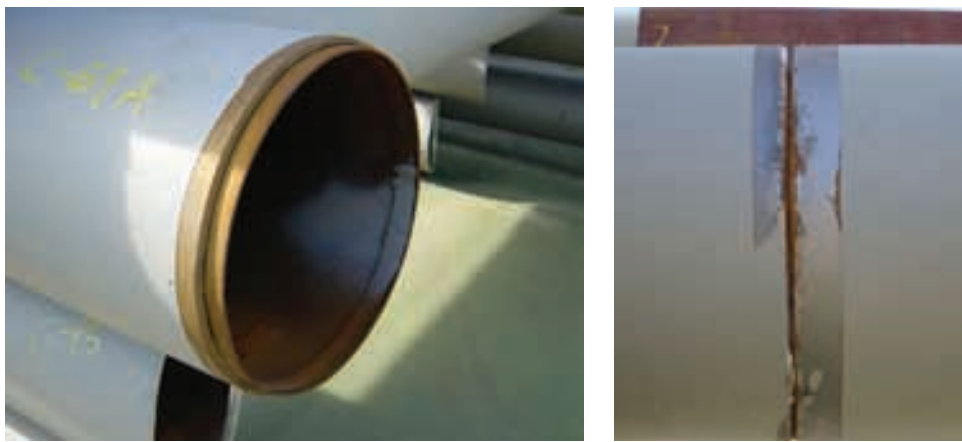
Soldaduras en línea. Preparación de la camisa y unión.
